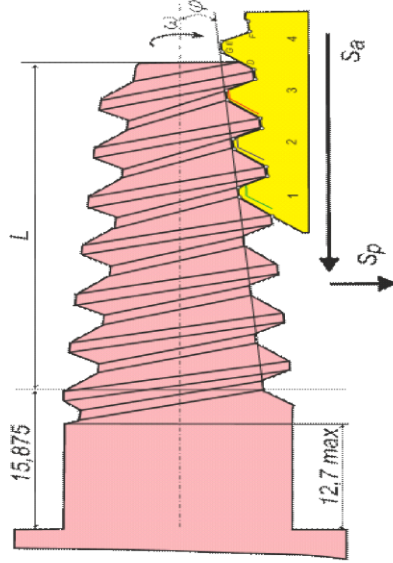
Схема початку фінішного проходу 4-рибкової гребінки під час виконання замкової нарізні. Sa - повздовжня подача гребінки, Sp - поперечна подача гребінки, omega - рух обертання заготовки навколо осі.
